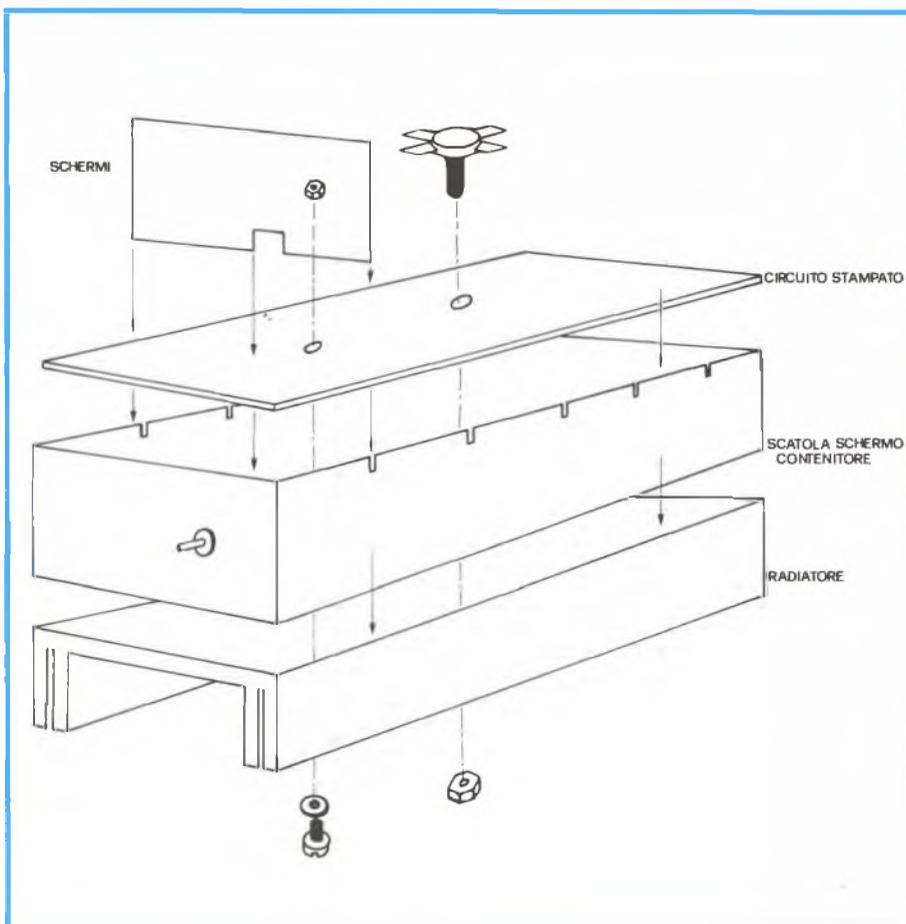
Assemblaggio meccanico generale del dispositivo.
